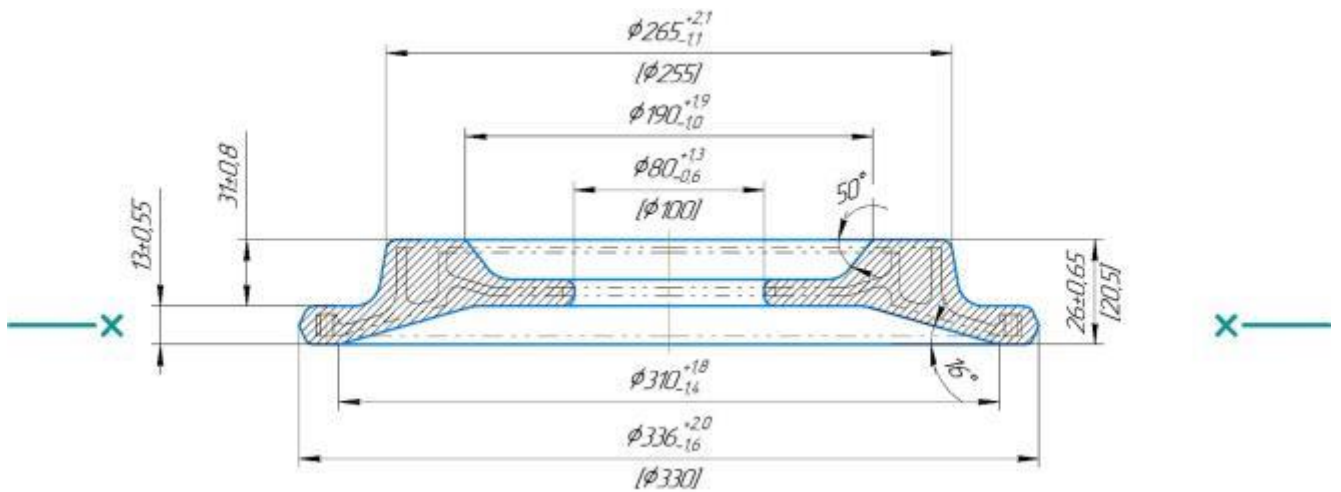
Ескіз заготовки, що отримана штамповкою на КГШП
